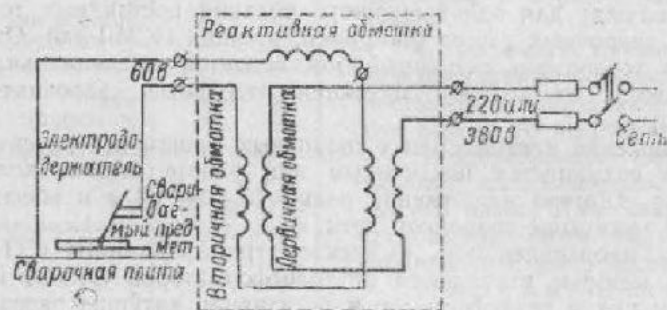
Принципиальная схема сварочного трансформатора с реактивной катушкой.
